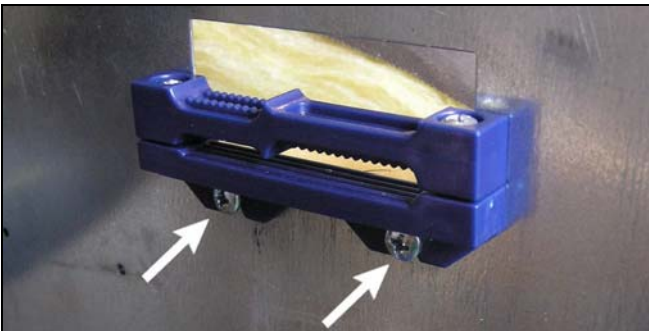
Montieren Sie die Zugentlastung vor der Kabeldurchführung mit zwei Blechschrauben an der Kesselverkleidung hinten.
